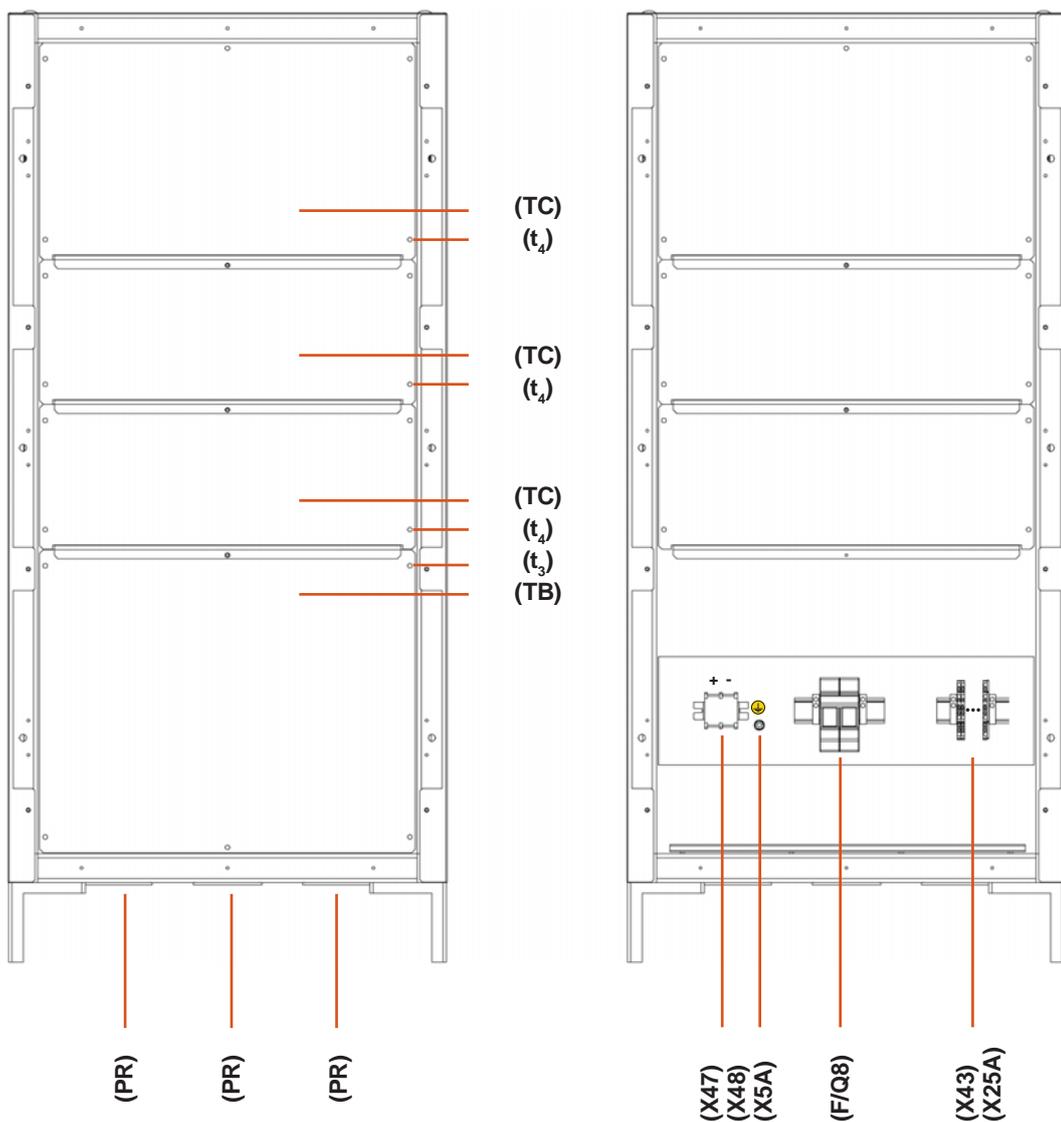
Vue frontale armoire de batteries de 605x605x1315 mm.
